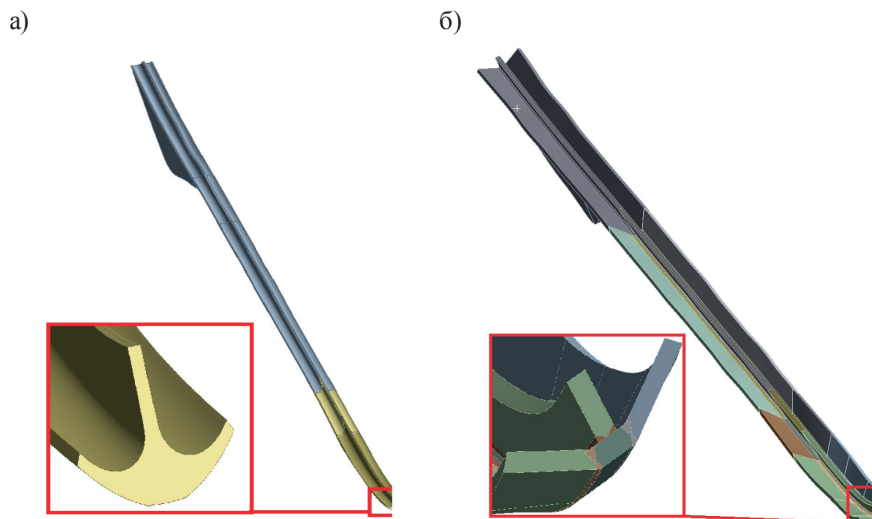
Модели литого (а) и сварного (б) форштевней
